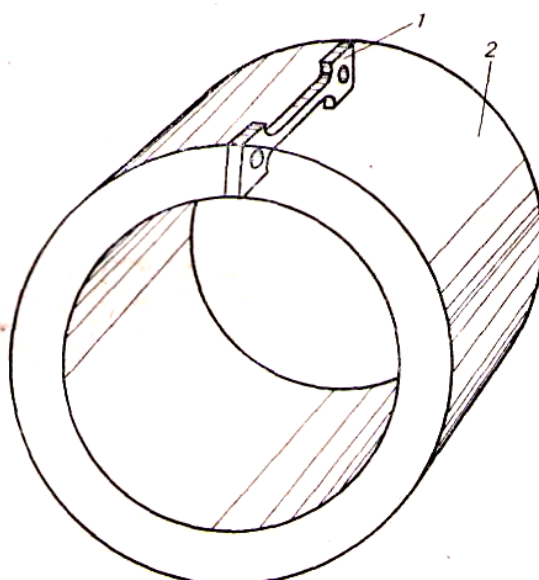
Схема вырезки образцов из наплавленного металла
